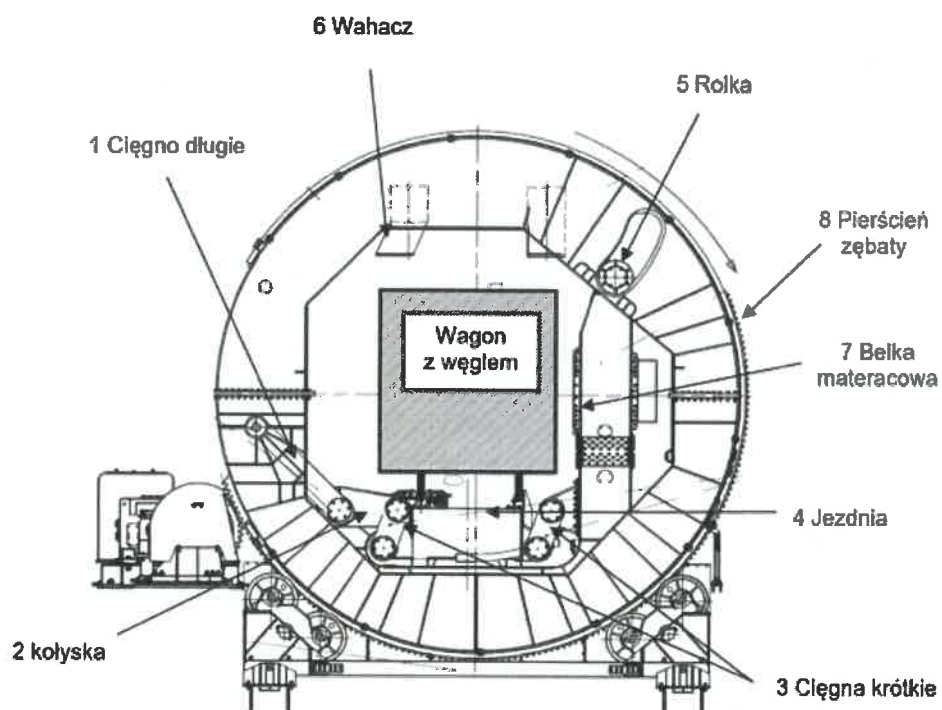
Schemat elementów konstrukcji beczki wywrotnicy wagonowej widok od strony wjazdu
